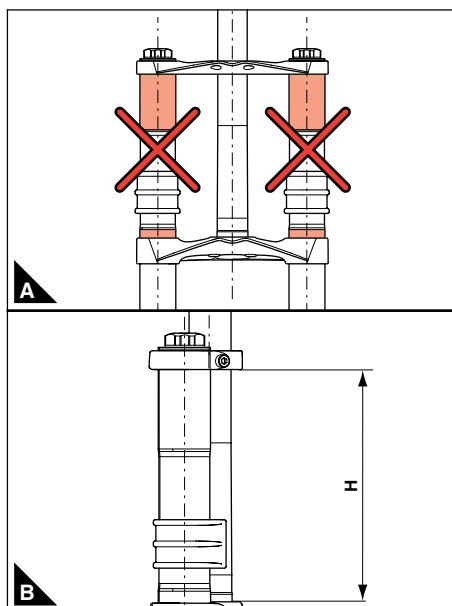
Installazione sul telaio di forcelle a doppia piastra: (2A) Fissaggio piastre di sterzo, (2B) Lunghezza massima canotto di sterzo tra le piastre
